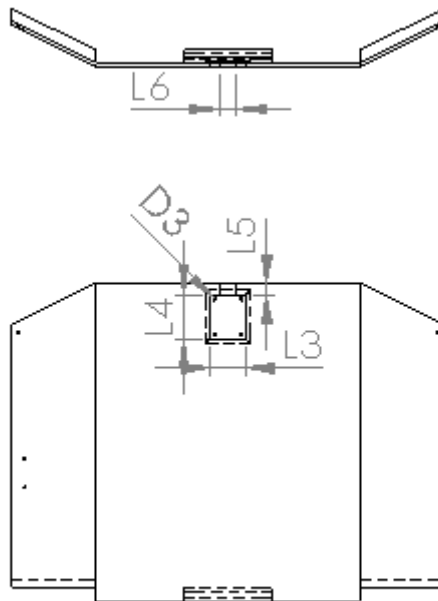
Corquis de dimensiones. Elemento 1.1.2.1.
